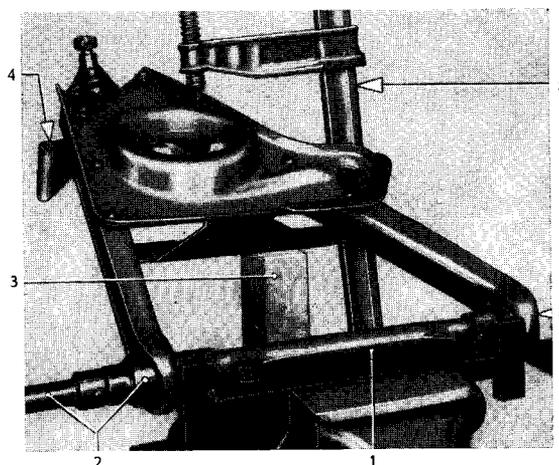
Lenker zum Einschrauben der Gewindebuchsen festgespannt
